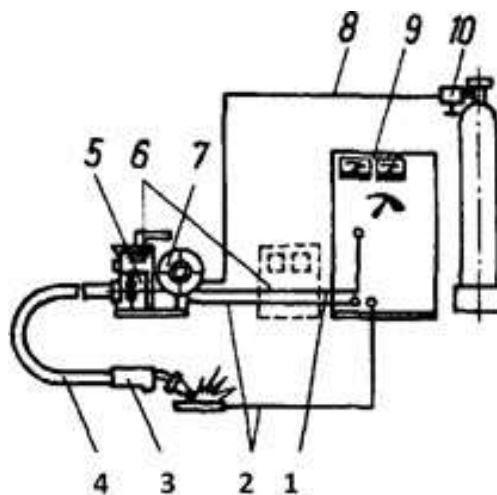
Схема напівавтомата для зварювання в захисних газах:
